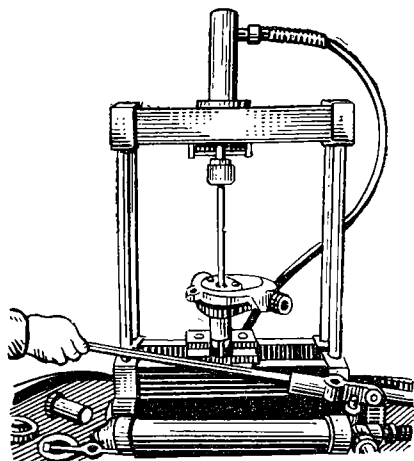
Выпрессовка валика водяного насоса с помощью гидравлического пресса ГП-20
